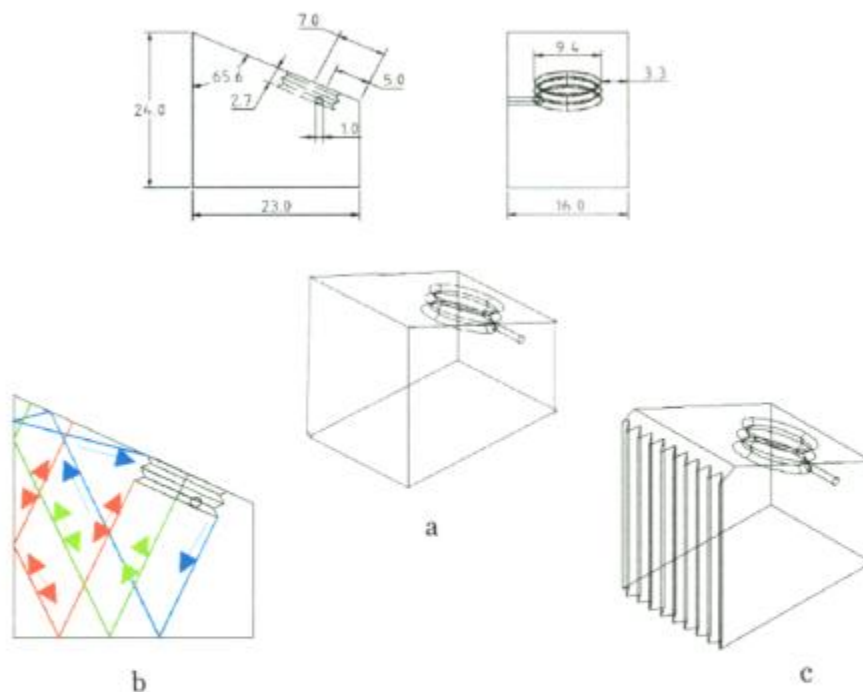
Detalle de la construcción para el transductor MSWQC-5: a) dimensiones, b) posibles reflexiones dentro del plástico, c) forma definitiva de la zapata.
